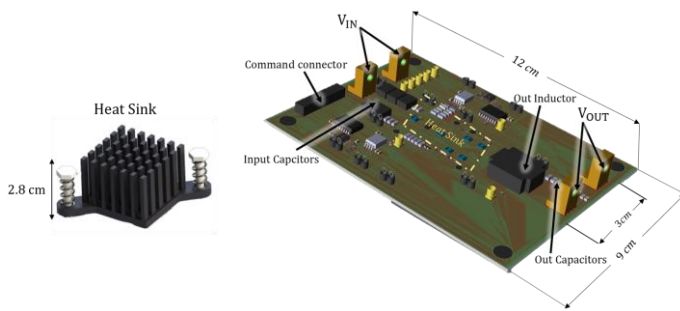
Vue 3D du PCB routé intégrant le volume des composants ainsi que les dissipateurs thermiques.
